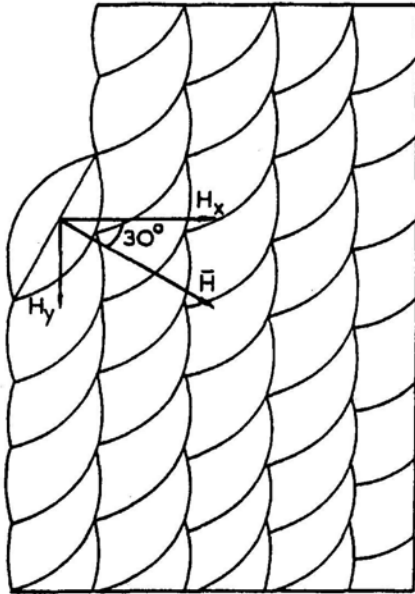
Direction du flux thermique pour une soudure horizontale-verticale [16].
